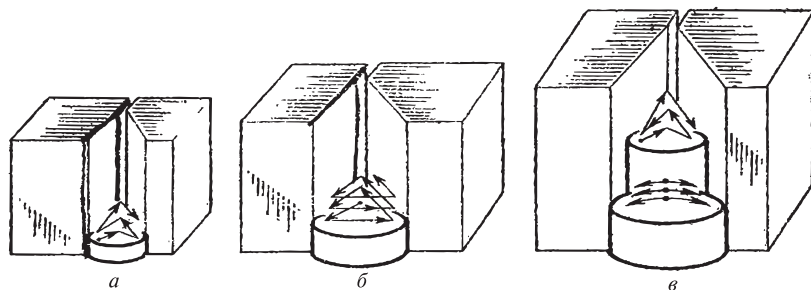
Схема выполнения вертикального сварного шва
